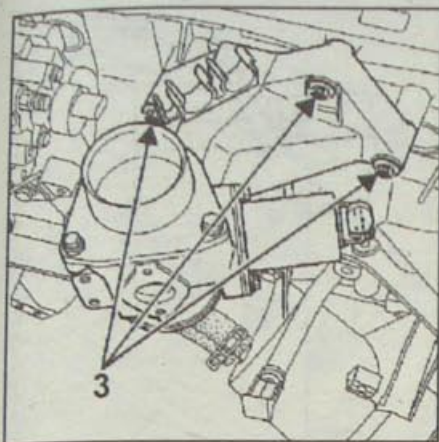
Расположение болтов (3) крепления корпуса остановки двигателя
